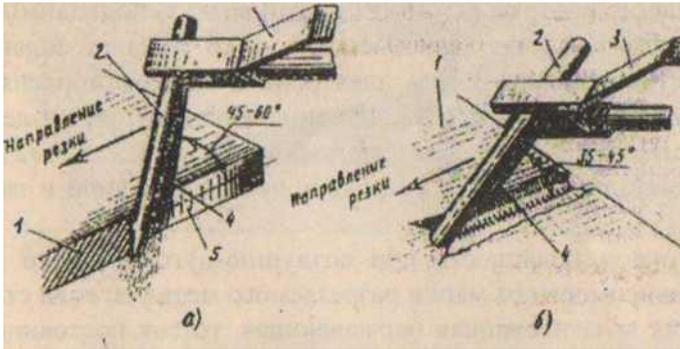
Схема разделительной (а) и поверхностной (б) резки
